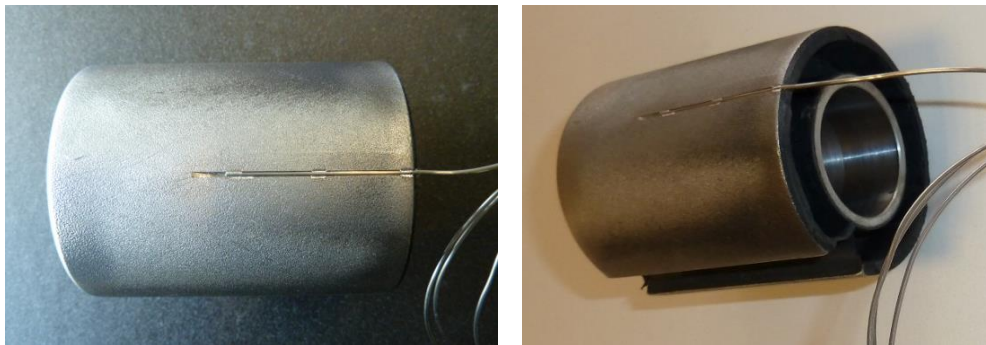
GM-Teil mit eingeschweißten Thermoelement
